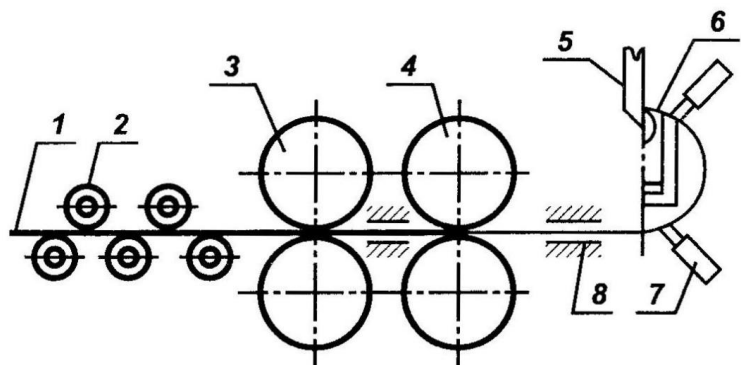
Схема дії автомата для безоправочного навивання пружин: 1–дріт; 2–правильні ролики; 3 і 4–транспортуючі ролики; 5–ніж; 6–упор; 7–пальці; 8–напрямні
